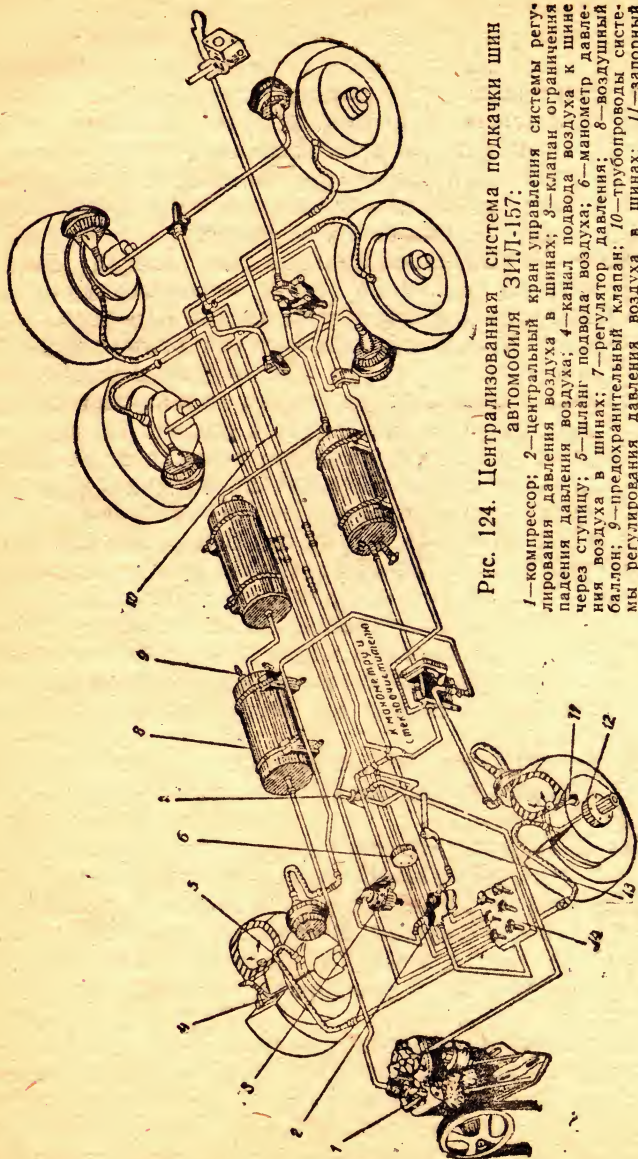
Централизованная система подкачки шин автомобиля ЗИЛ-157;
